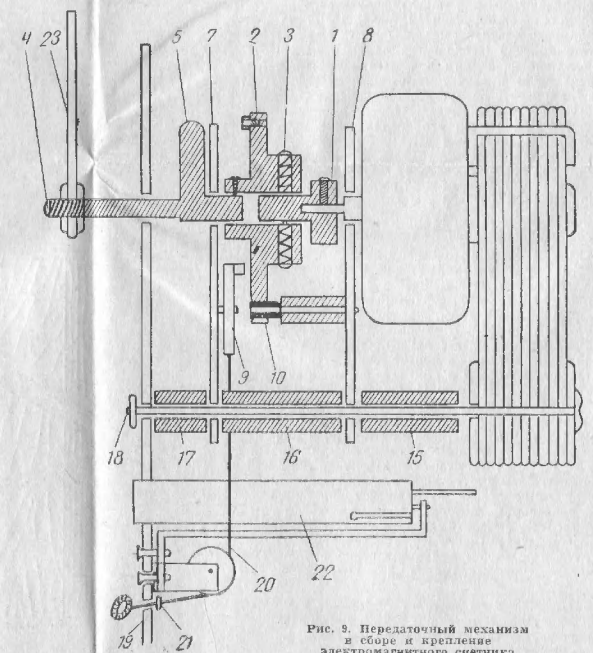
Передаточный механизм в сборе и крепление электромагнитного счетчика
